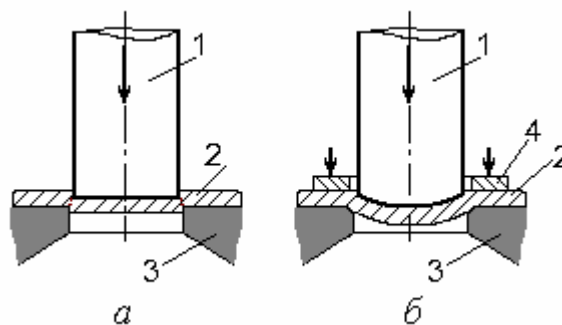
Схема пробивки (*а*) и вытяжки (*б*):
